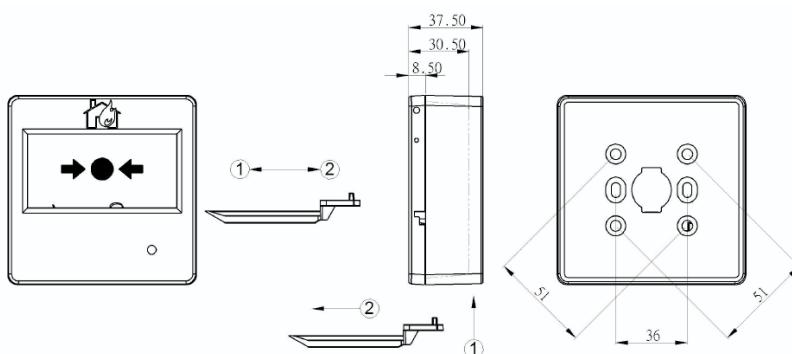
Dimensioni - Dimensions - Dimensiones - Dimensões
